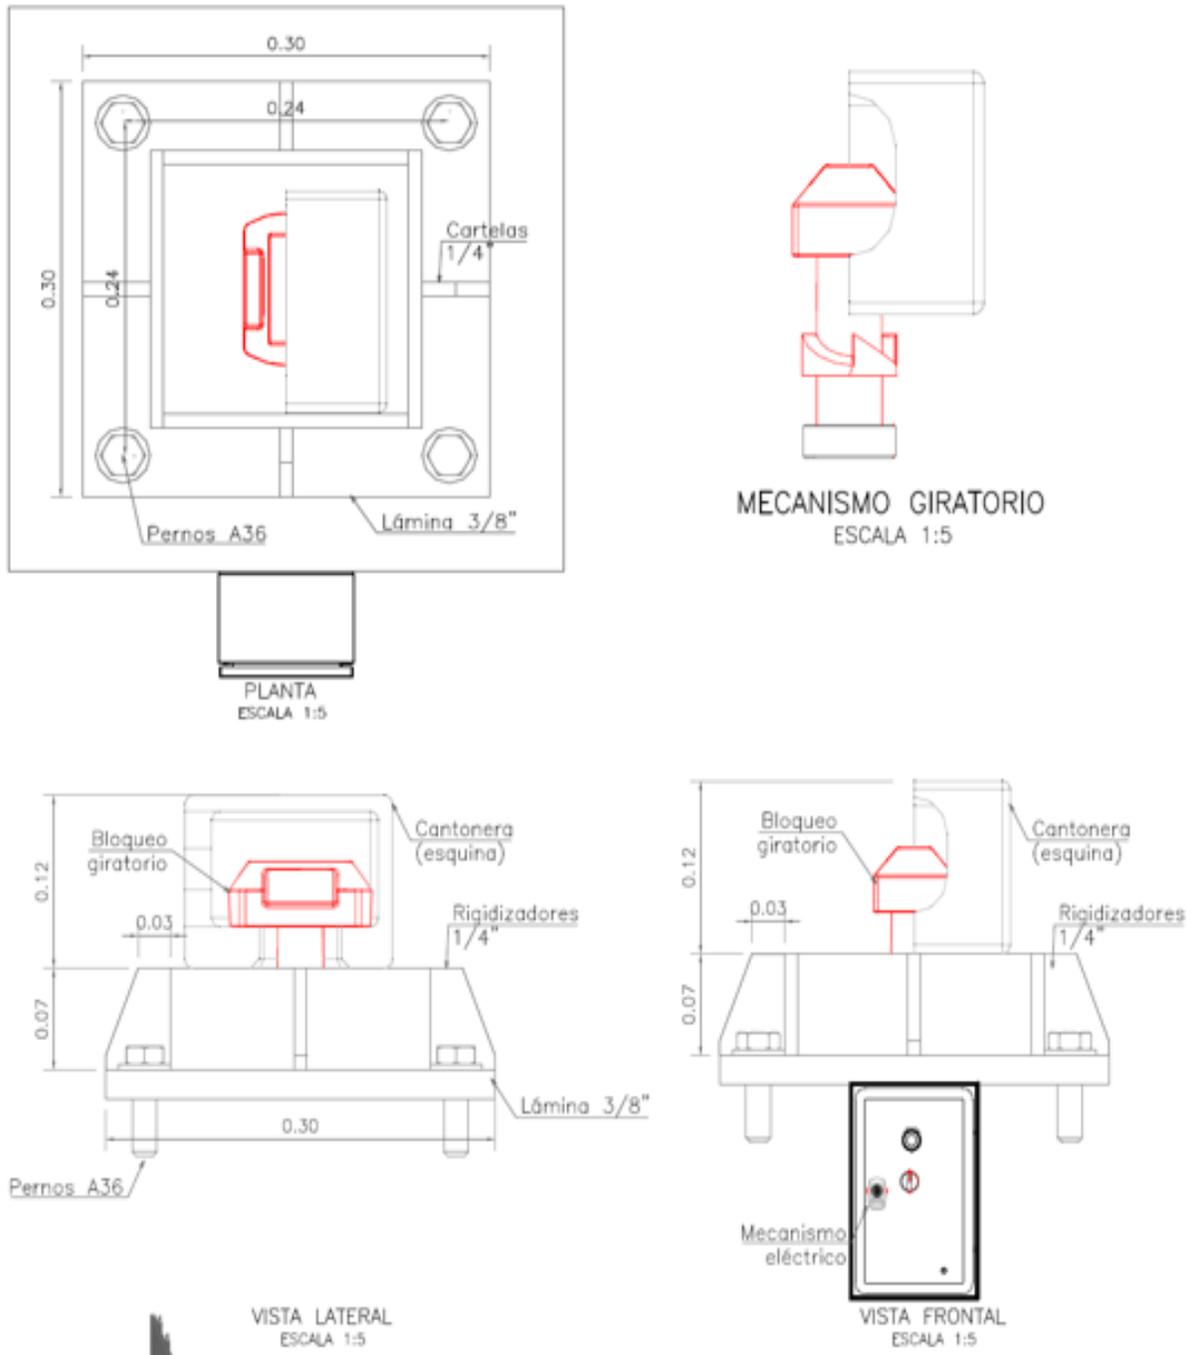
Planta y secciones del mecanismo de anclaje para contenedores. Elaboración propia. 2021.
